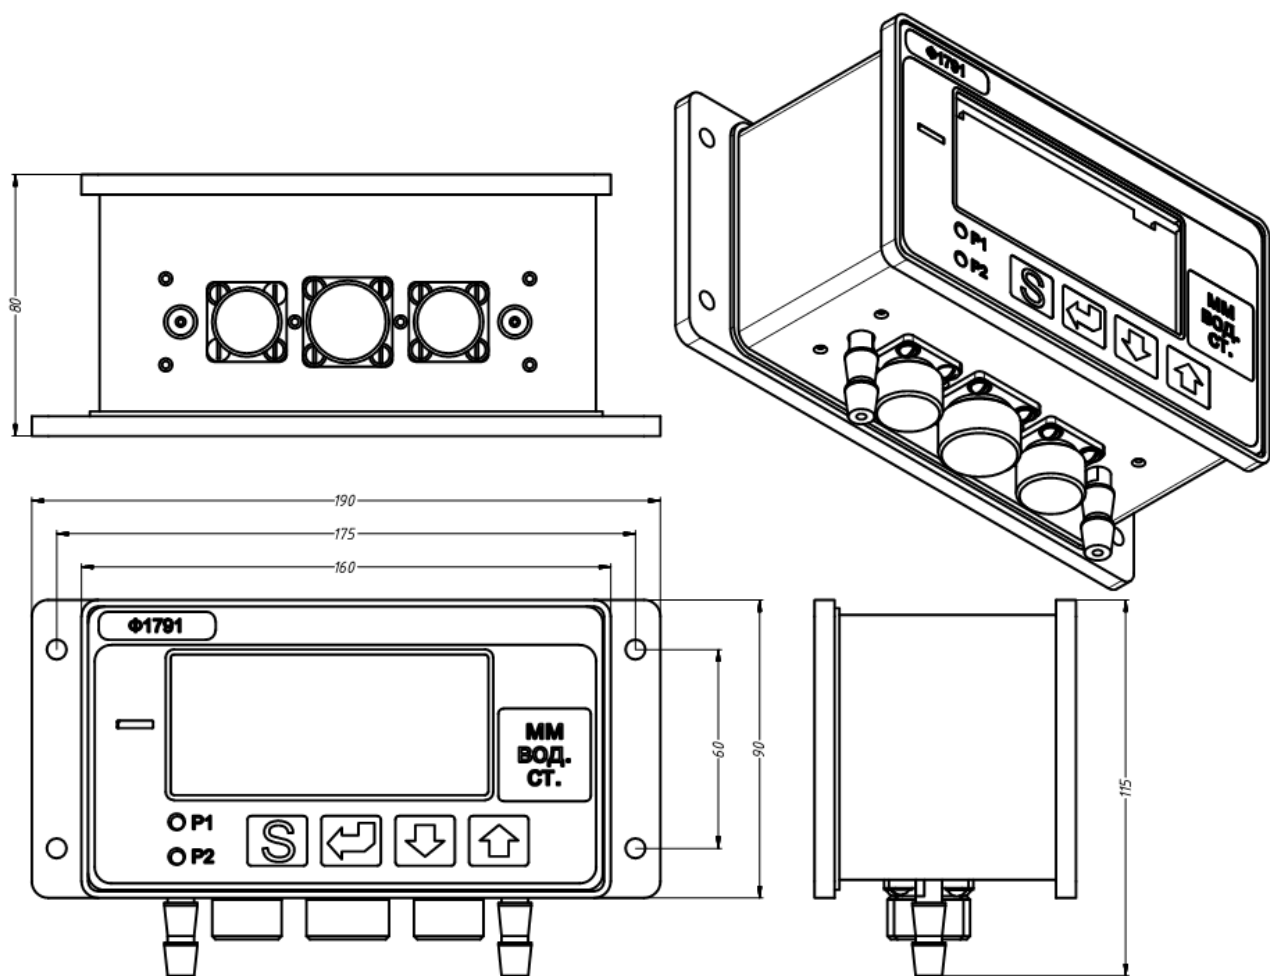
Внешний вид и габаритные размеры Ф1791.2
